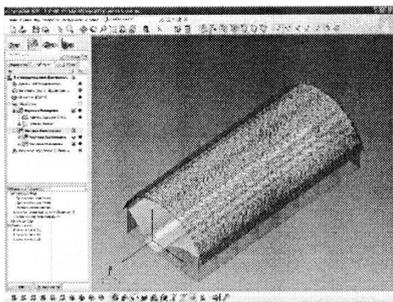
Траєкторія руху інструмента на операції чистової обробки деталі
